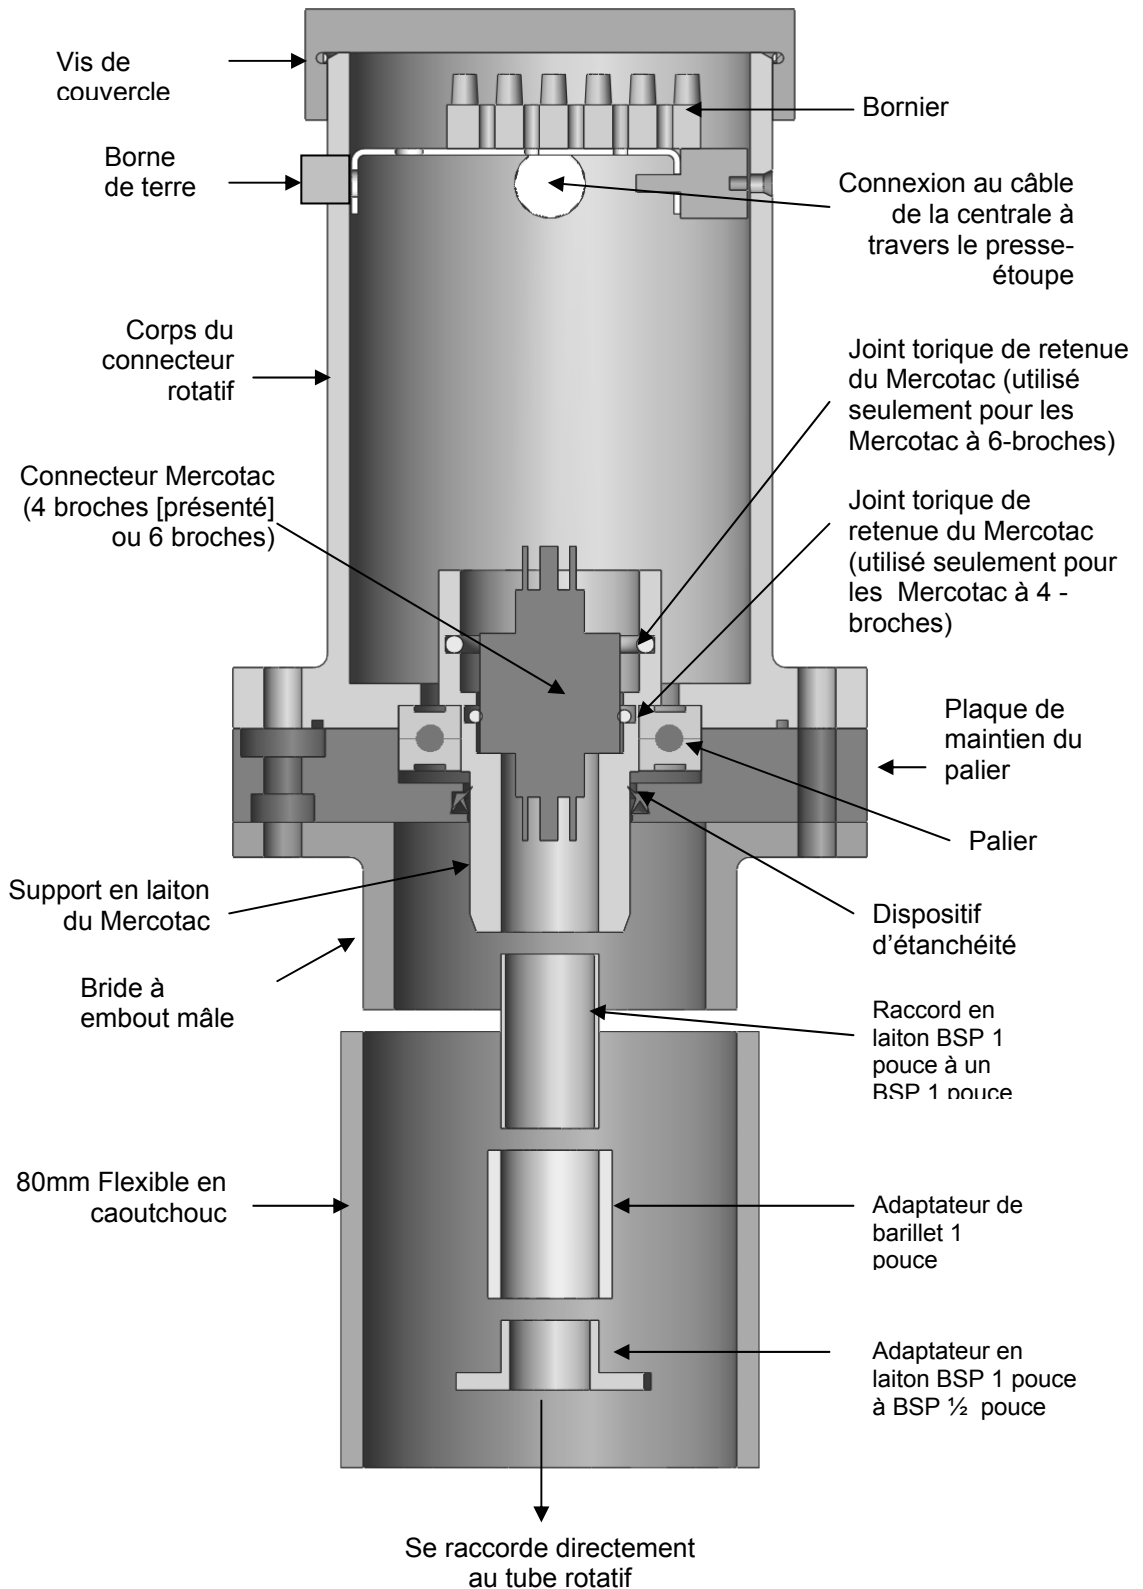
Assemblage de connecteur rotatif de type 'C'
